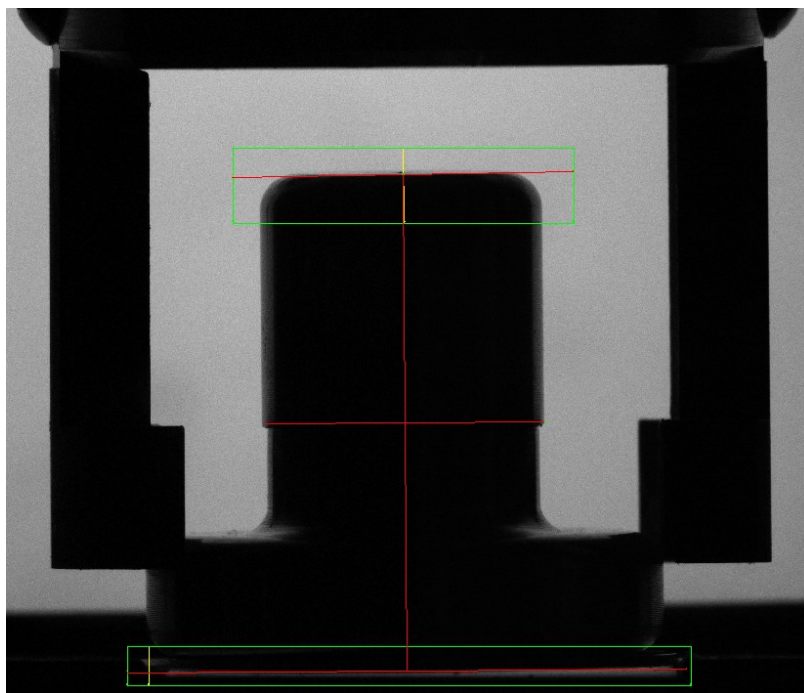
Rozsáhlá skupina tříd funkcí k detekcím a testování – Machine Vision
